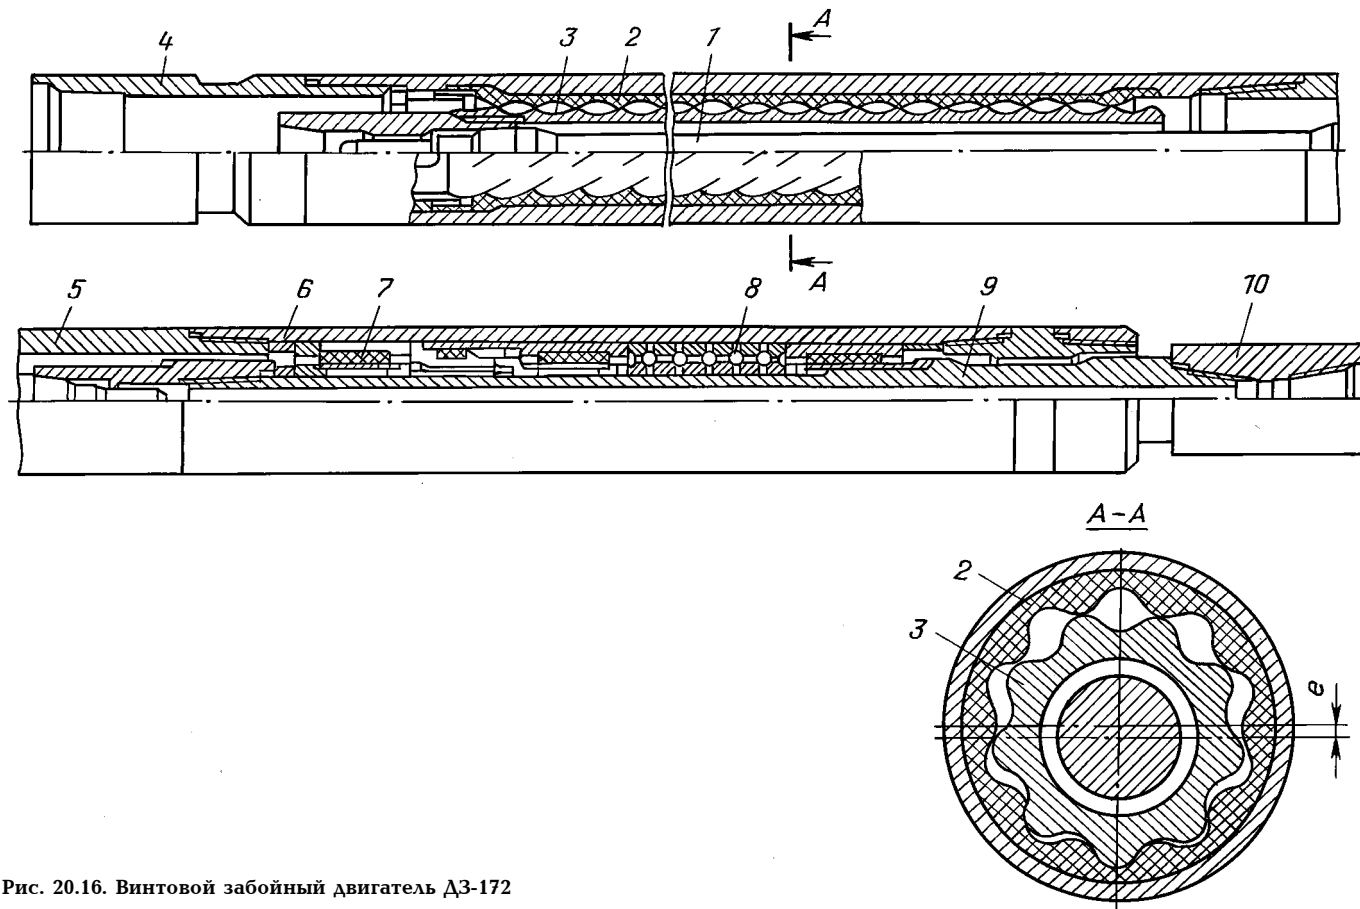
Винтовой забойный двигатель ДЗ-172
